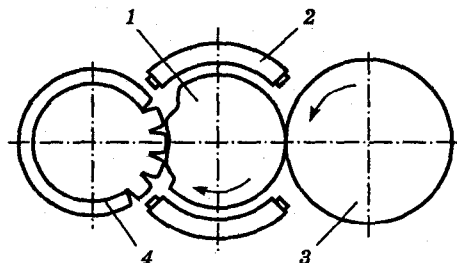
Схема накатывания зубчатых колес с радиальной подачей валков
